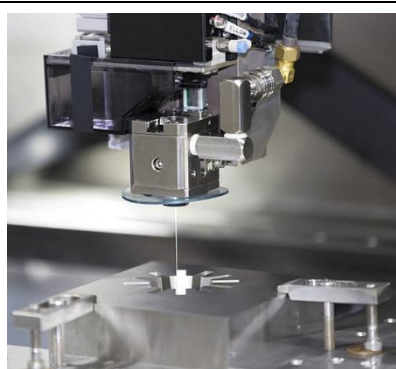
Stroj pro obrábění ultrazvukem.
